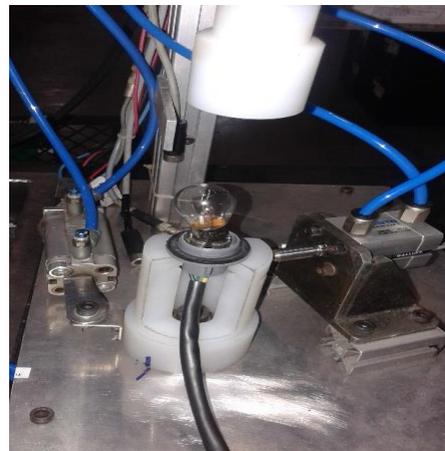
Lâmpada posicionada para o dispositivo inserir.
